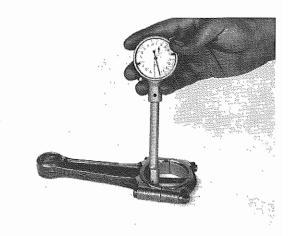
Controllare il gioco radiale Checking radial clearance
